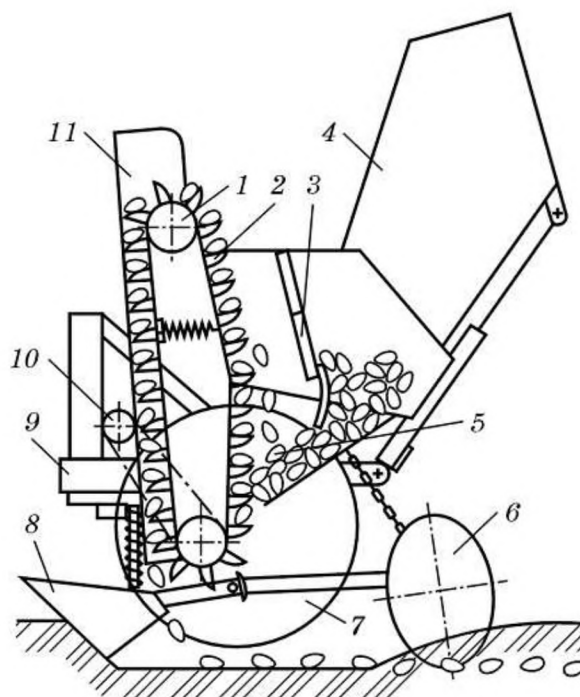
Функціональна схема картоплесаджалки: 1 - садильний апарат; 2 - ложечка; 3 - бункер; 4 - заслінка; 5 - живильний ківш; 6 - дисковий загортач; 7 - опорно-привідне колесо; 8 - сошник; 9 - рама; 10 - механізм приводу; 11 – кожух
